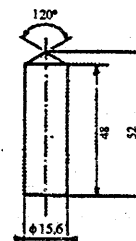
pistón cilíndrico de bronce dimensiones en mm.
